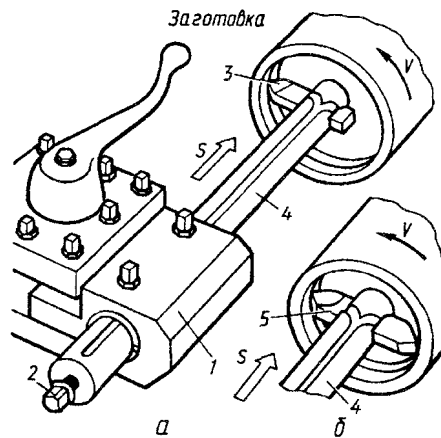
Універсальна розточувальна оправка до токарного верстата: а - розточування прохідним різцем; б - розточування мірною пластиною: 1 - допоміжний тримач; 2 - гвинт; 3 - прохідний різець; 4 - оправка; 5 - мірна розточувальна пластинка
